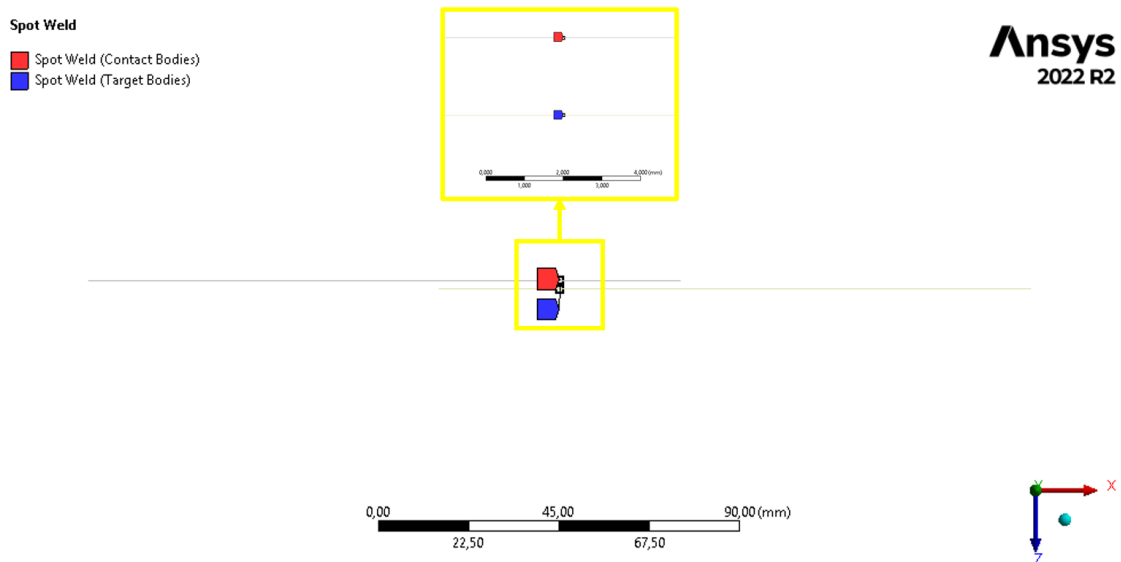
Vista de perfil del contacto Spot Weld
